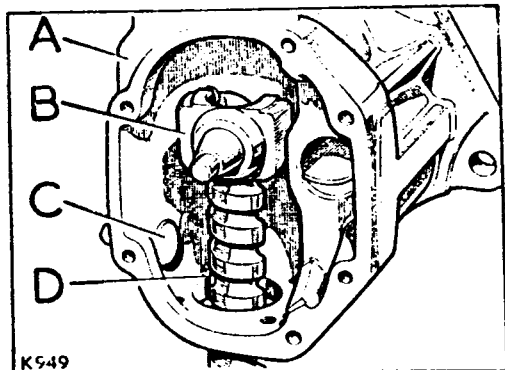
Montaje de la tuerca de bolas circulantes.
